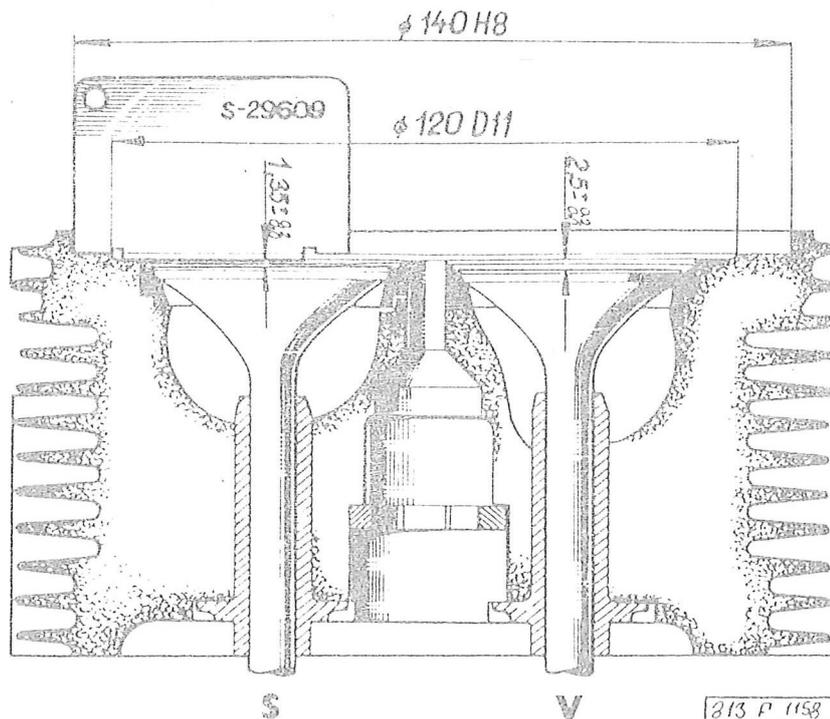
Abmessungen für die Bearbeitung des Zylinderkopfes
